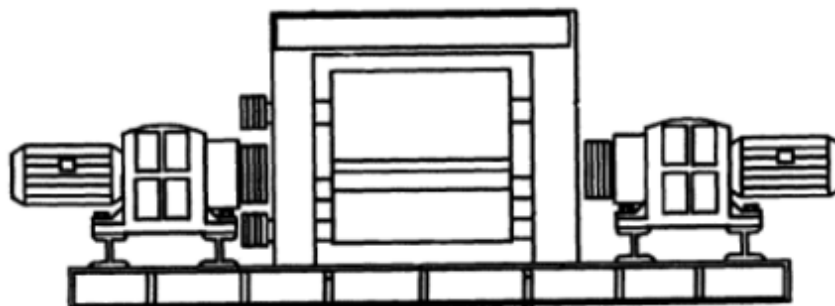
Валкова дробарка з використанням двох редукторів
